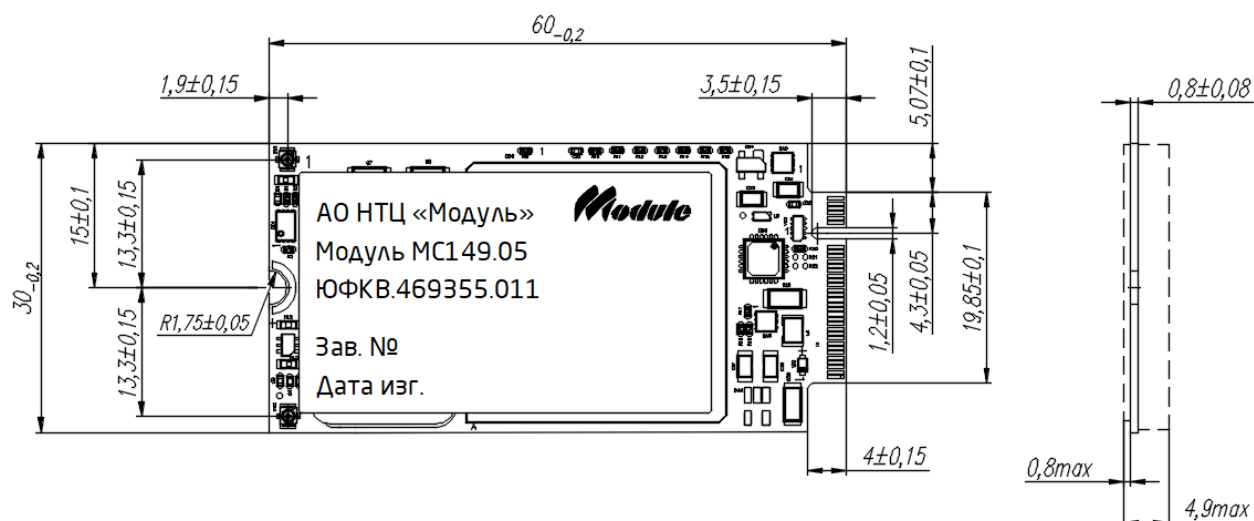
Габаритные и присоединительные размеры Модуля
